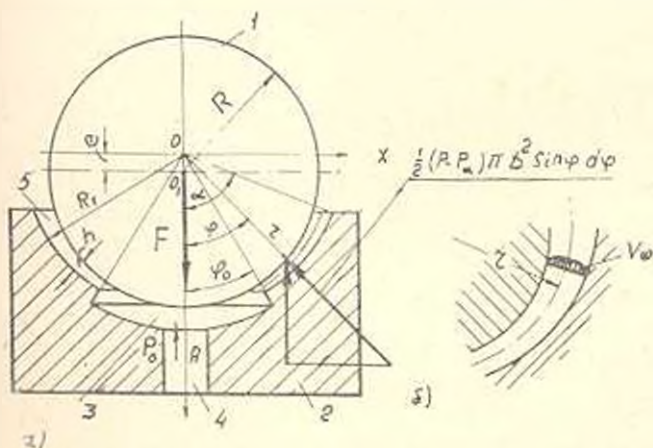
а) — Схема сферического подшипника с воздушной смазкой; 1 — шар, 2 — чашка, 3 — карман, 1 — входной канал, 4 — криволинейный зазор, б) — Распределение скорости по толщине слоя смазки
